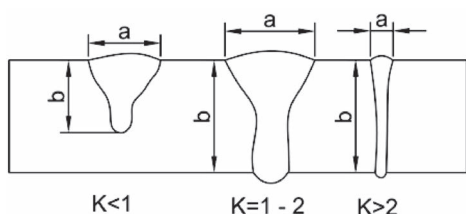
Виды сварных соединений, выполненных методом лазерной сварки
